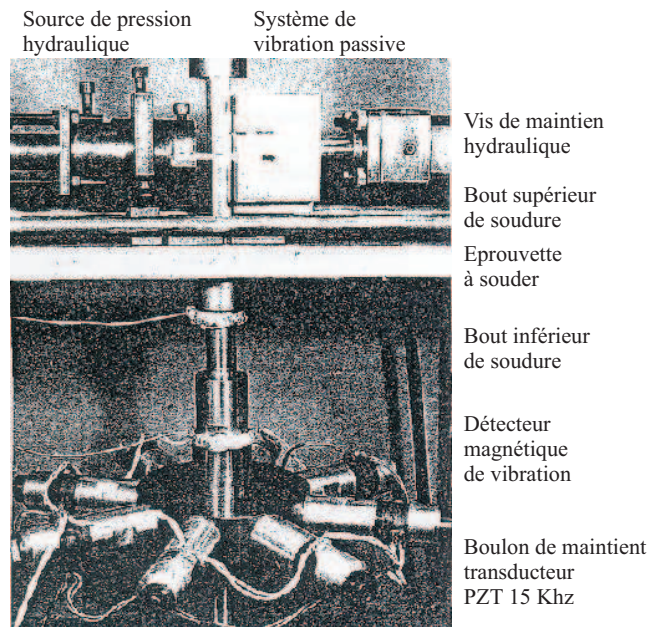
Ensemble acoustique pour le soudage bout à bout à la fréquence 15 KHz [5, 9, 10]
